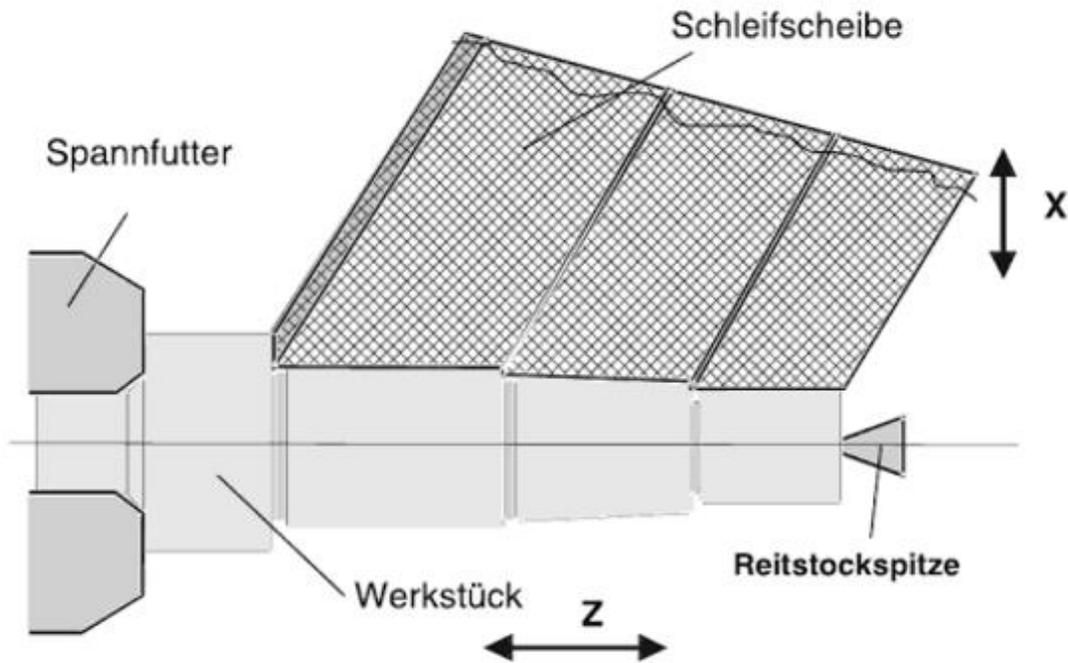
Arbeitsbeispiel einer Wellen-Komplettbearbeitung auf einer CNC-Schrägeinstech-Schleifmaschine mit einer durch eine Diamant-Abrichtrolle profilierten Schleifscheibe^[7]
